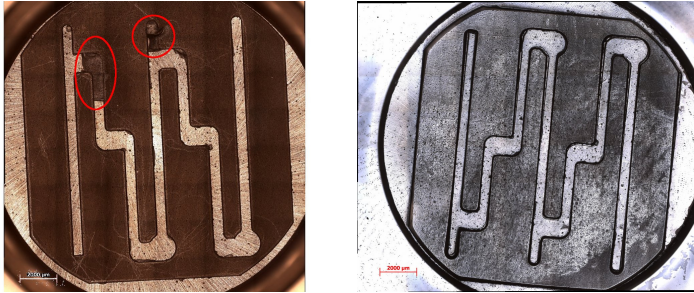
links: Mikroskopische Aufnahme des Werkzeugs des Durchflussanalysystems (Ausbrüche im Werkzeug rot markiert); rechts: eine mit Chrom beschichtete geprägte Probe
